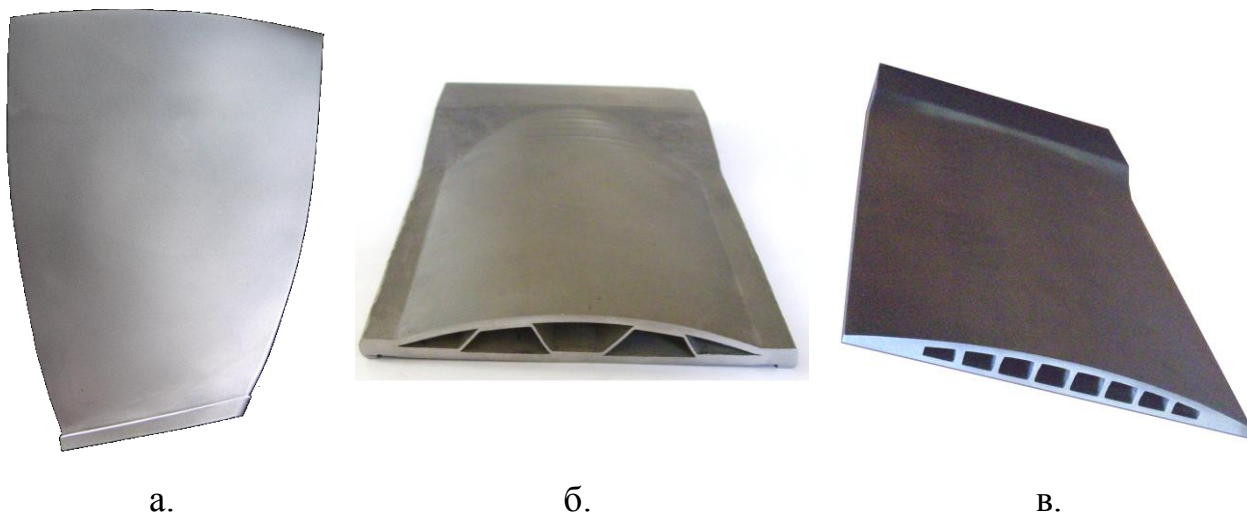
Конструкторско-технологические решения изготовления полых лопаток из сплава ВТ6: а – готовая лопатка полый конструкции; б – макет лопатки с наполнителем ферменного типа; в- макет лопатки с наполнителем стрингерного типа.
